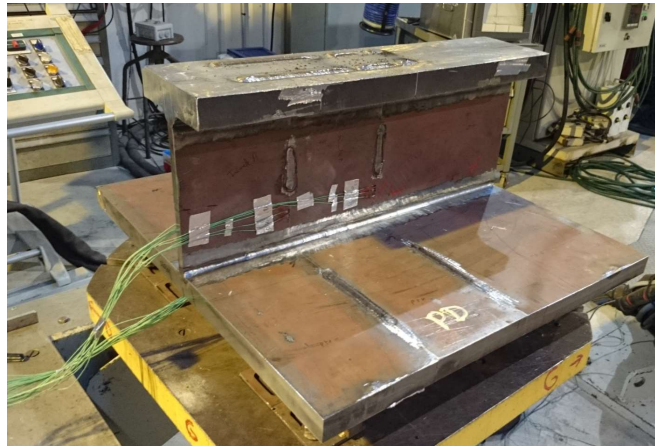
Positionnement de la maquette avant soudage MAG
